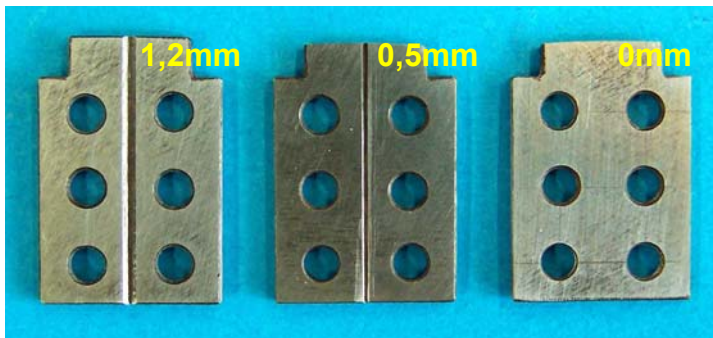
Zusätzliche Einsatzplatten für die Probenhalter
